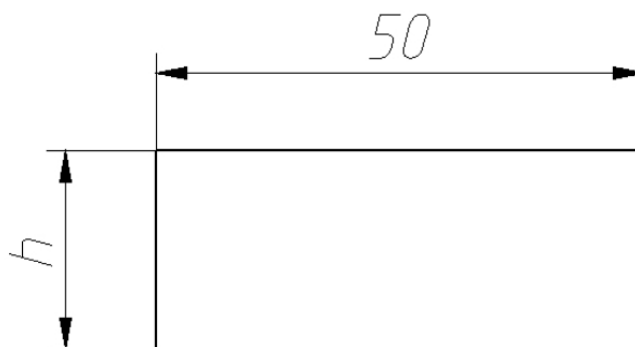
Имитатор усиления сварного шва; h – толщина
